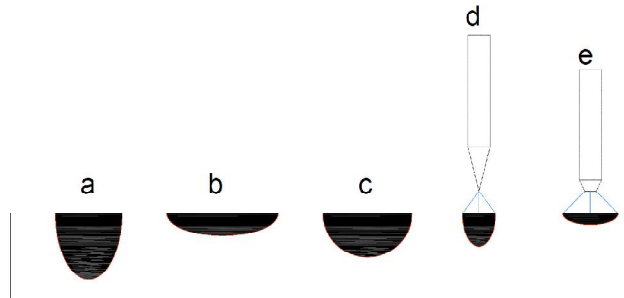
Akım türü ile elektrod ucunun aldığı şekiller [17]
